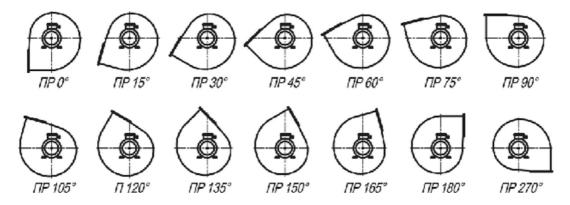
Схема разворотов корпусов тягодутьевых машин типа ВДН и ДН (ПР).
